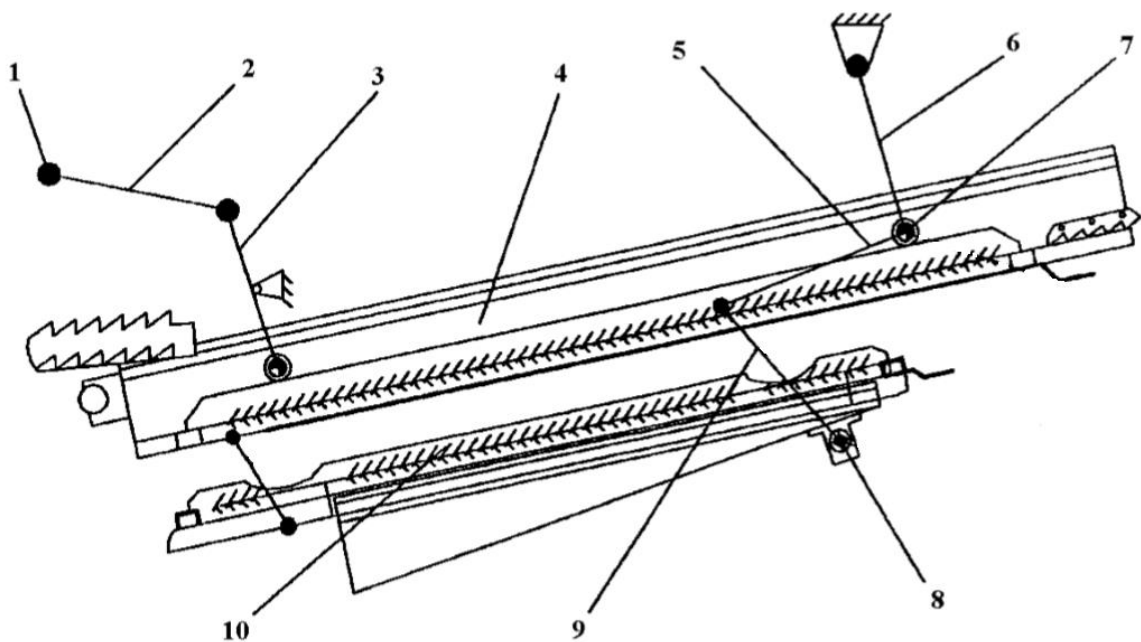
Механізм коливання решіт: 1 – опорні підшипники коливального валу; 2 – шатун; 3 – приводний важіль; 4 – верхнє решето; 5,6 – підвіска; 7 – задня вісь кочення верхнього решета; 8 – нерухома вісь кочення важелів решіт; 9 – двоплечий важіль; 10 – нижнє решето.
